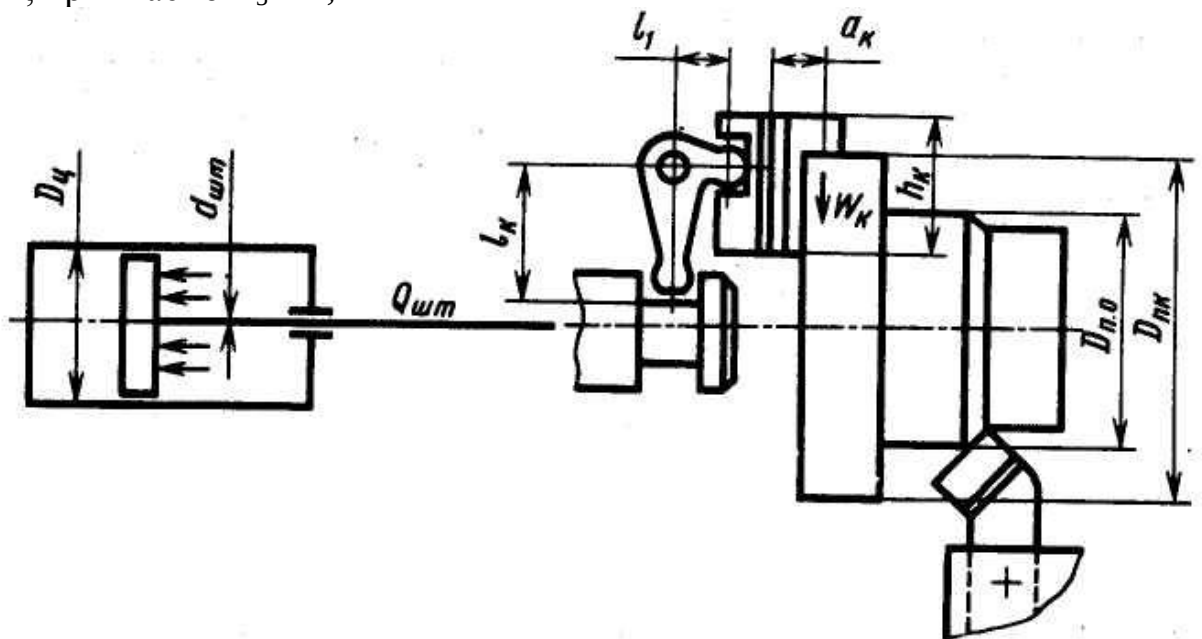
Схема обробки поверхні зовнішнього діаметру деталі при використанні трьохкулачного патрону з пневматичним приводом затиску деталі.
